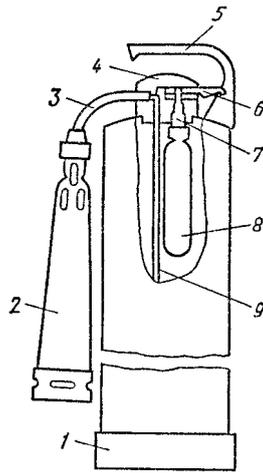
Огнетушитель воздушно-пенный ОВП-10: 1 – корпус; 2 – пенный насадок; 3 – трубка; 4 – крышка; 5 – рукоятка; 6 – пусковой рычаг; 7 – шток; 8 – баллончик со сжатым воздухом; 9 – сифонная трубка
